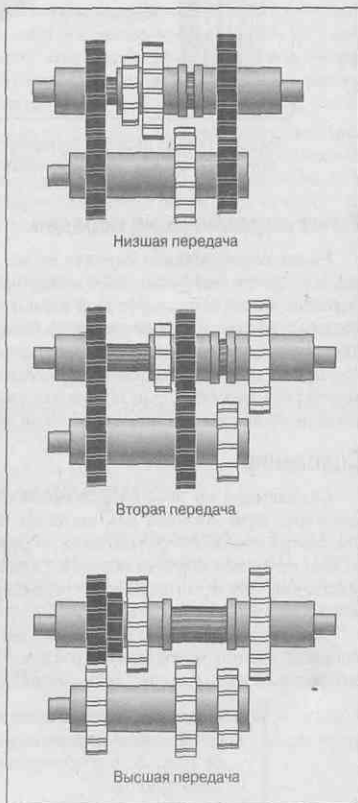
Шестерни трехступенчатой коробки передач в разрезе
